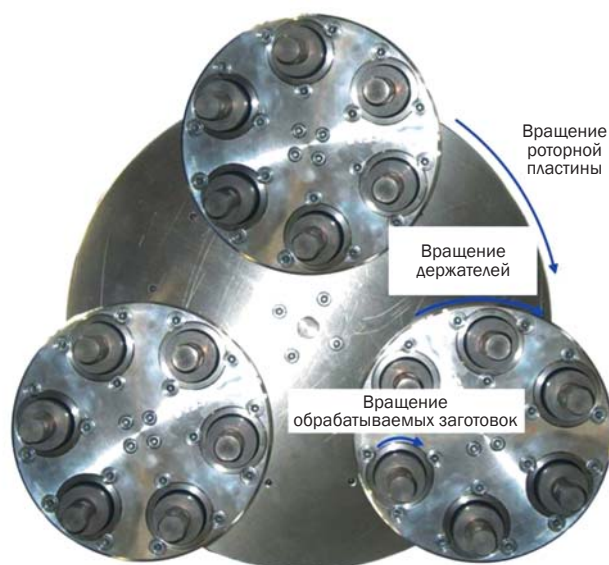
Принцип конструкции станка DF для чистовой обработки волочением от компании ОТЕС, показанной здесь с тремя головками, на каждой из которых можно закрепить до 6 обрабатываемых заготовок.
